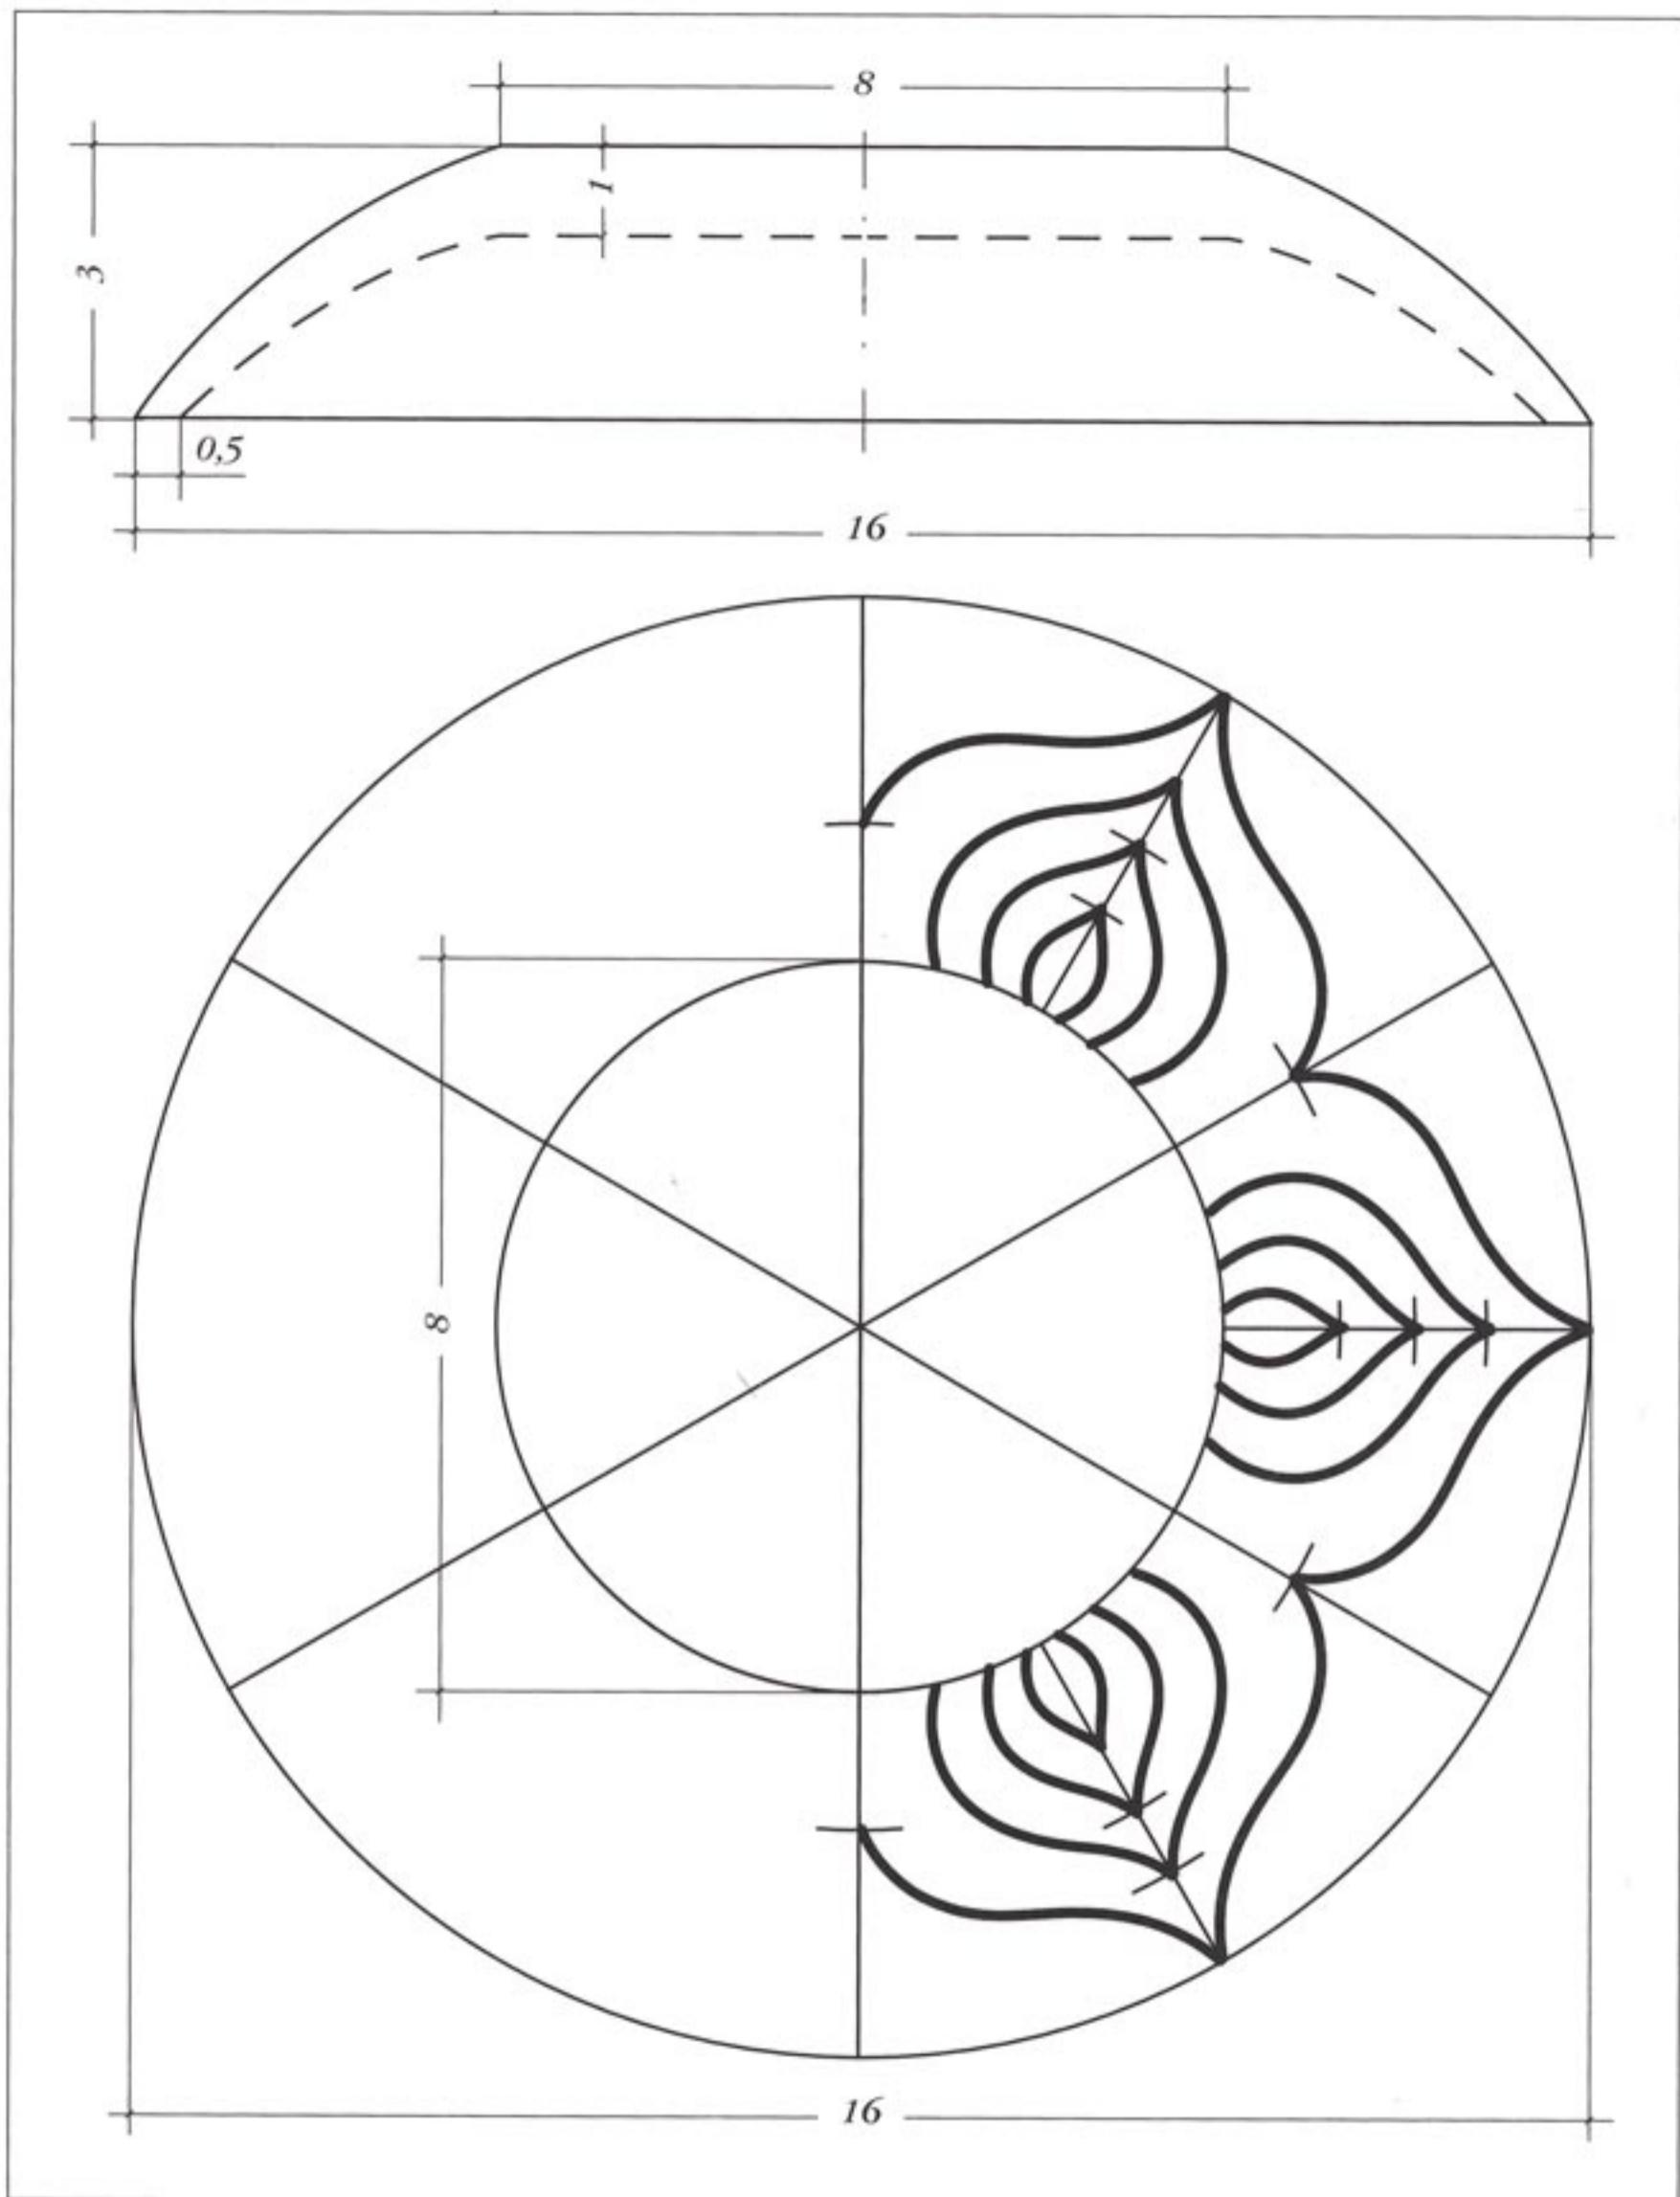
Чертеж и схема разметки нижней части цветка чаши-вазы к рис. 192
